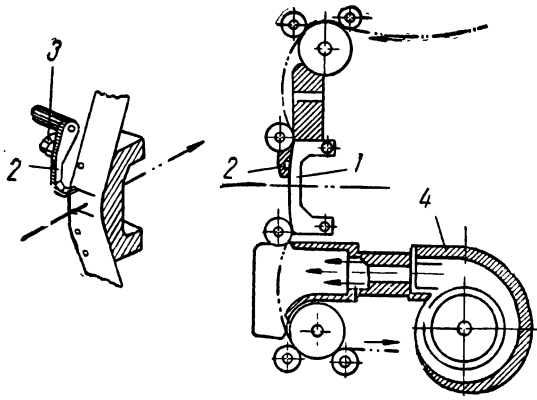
Схема пневматического скачкового механизма фирмы «Кодак»:
